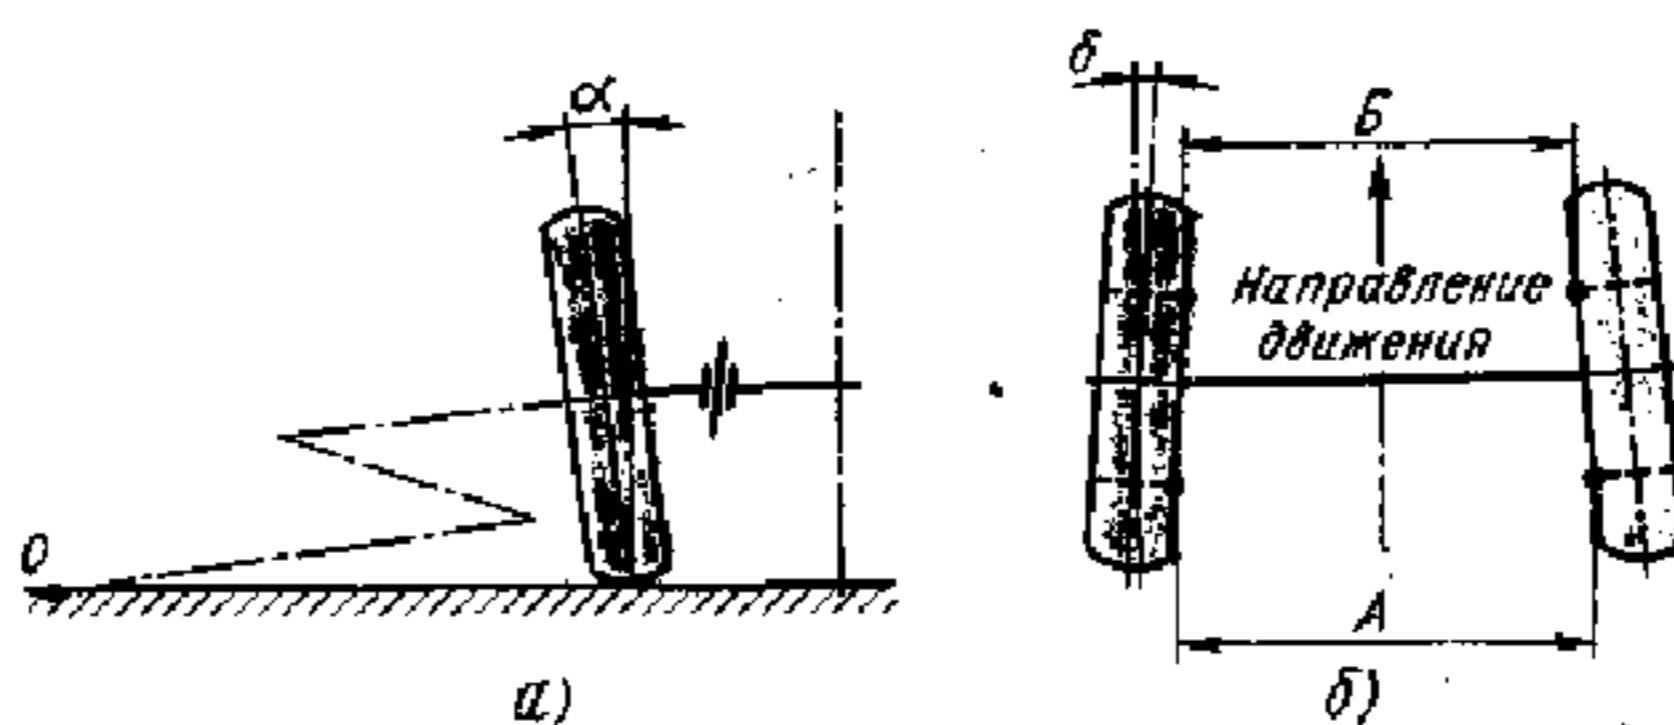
Углы установки управляемых колес: а — развал; б — схождение
